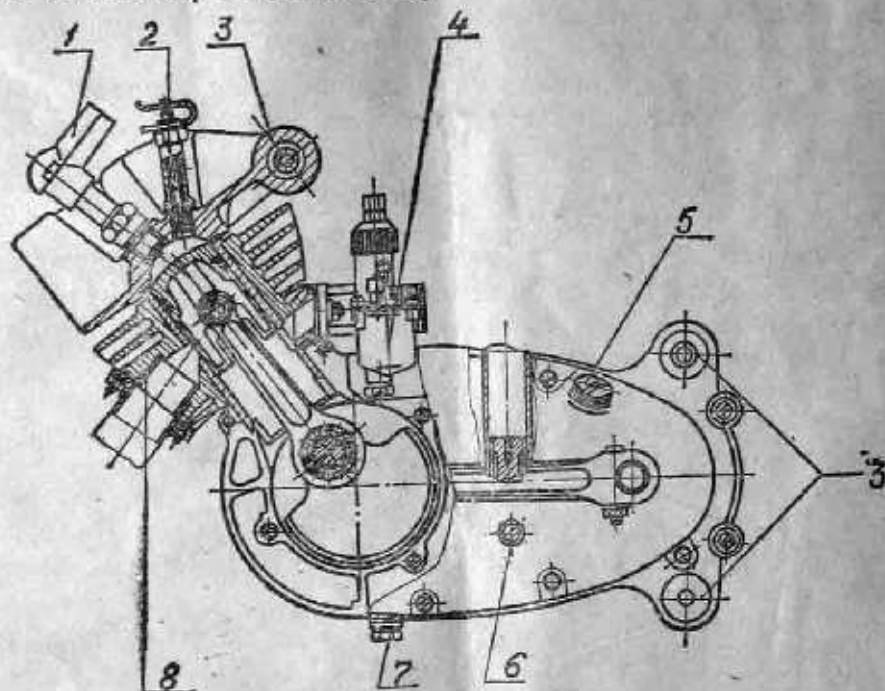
Двигатель Ш58 (Ш57), вид слева
